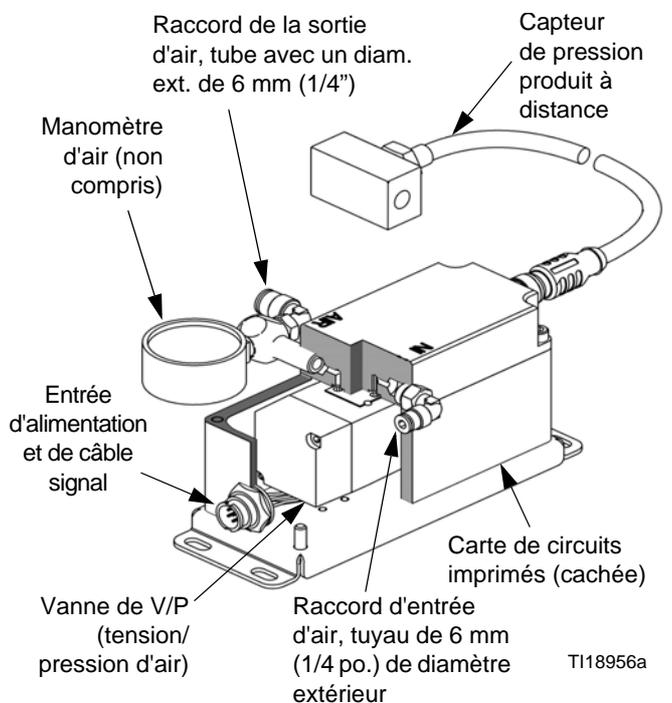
Vue en coupe du module de régulation de débit 24H989
